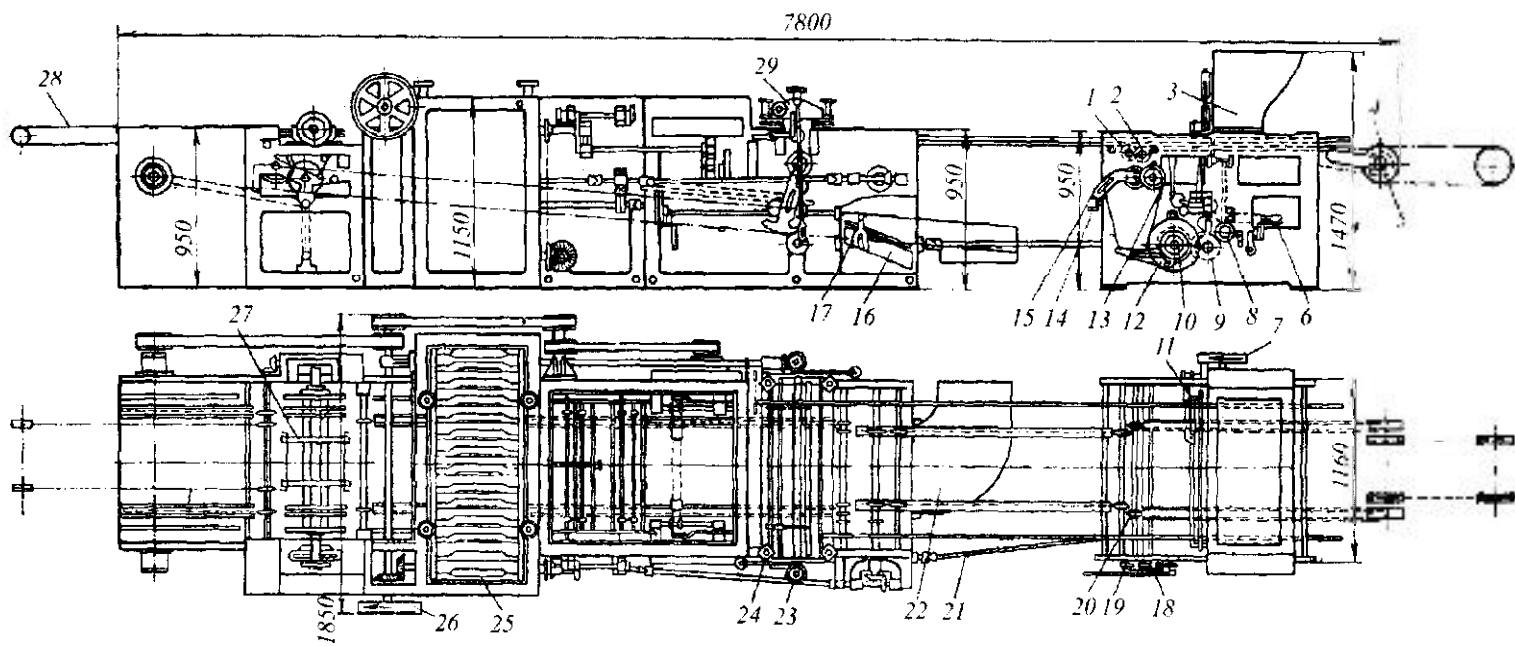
Конфетоотливочный агрегат с вертикальными мерными цилиндрами
